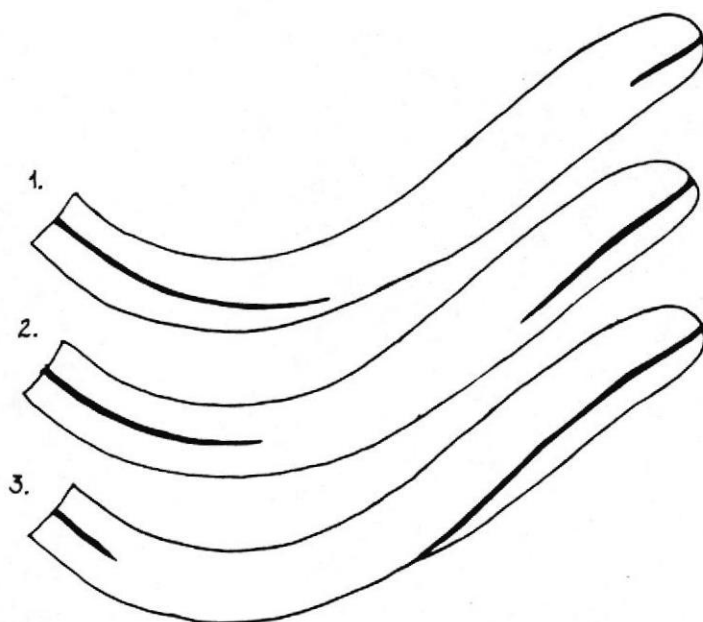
Reconstrucción de la orientación en hélice de la fisura en 1535.4; expuesto durante el desbaste de la sección longitudinal.
